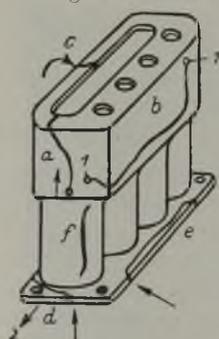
Autogene Schweißungen an einem Autoblockzylinder.
